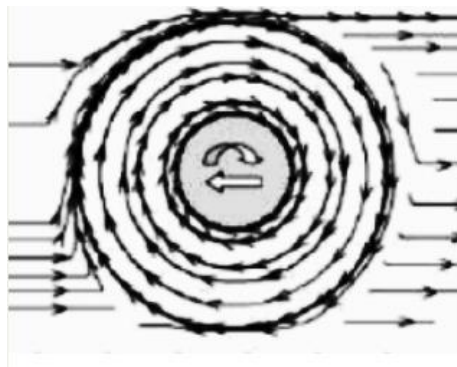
Flujo plástico de material en la soldadura FSW
